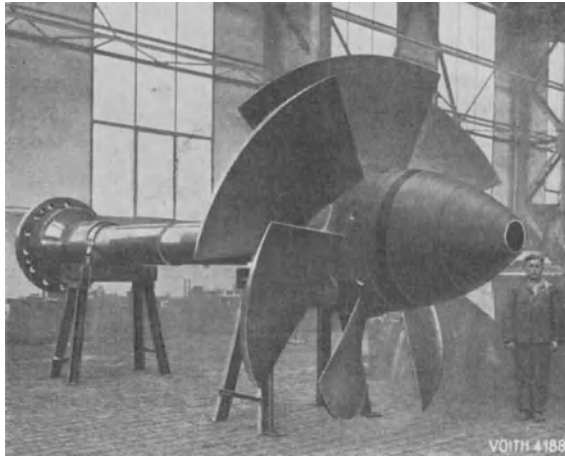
Kaplanrad mit sieben langen Flügeln für Gefälle bis 30 m.
